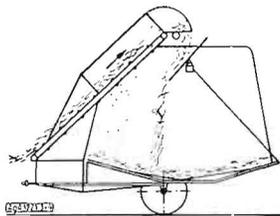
Klappe zum Einbringen des Strohpolsters hochgestellt
